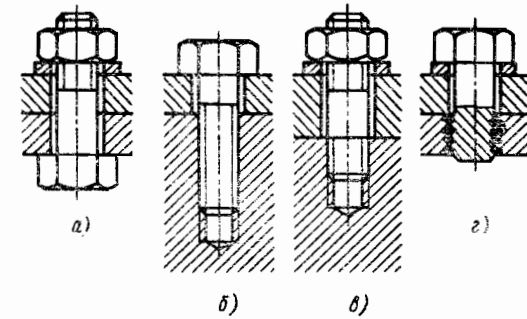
Основные типы резьбовых соединений: а — болт; б — винт; в — шпилька; г — со вставкой
